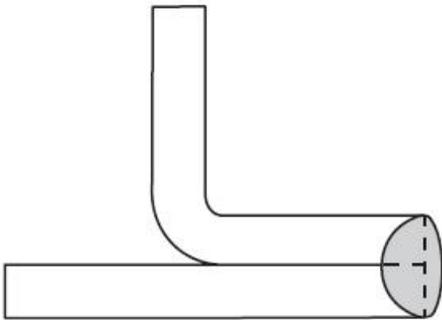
(Continua). - Juntas Soldadas Doble Ranura
